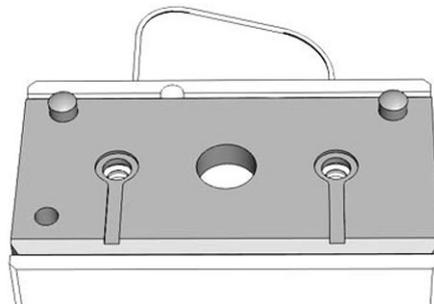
Tête de pompe avec plaque de rinçage des joints installée
